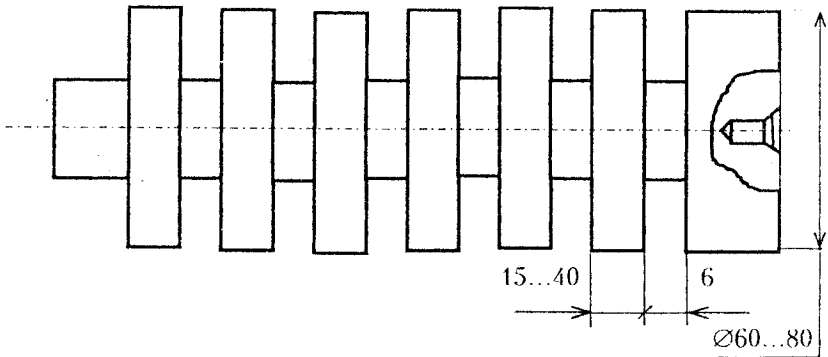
Загальний вигляд заготовки для проведення досліджень шорсткості обробленої поверхні
